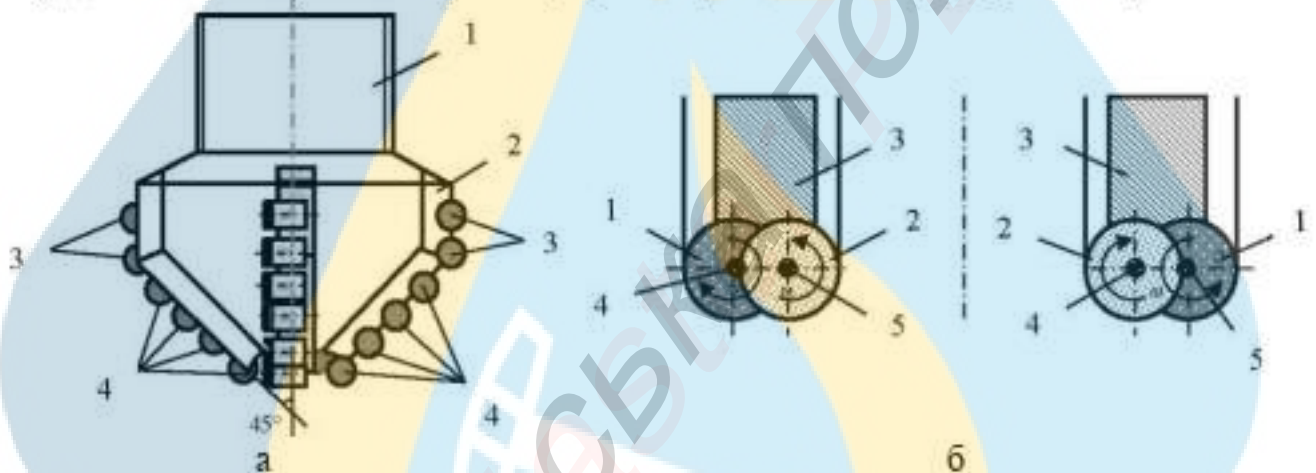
Породоруйнівний інструмент з обертовими при бурінні різцями типу PDC: а) бурове долото: 1 - корпус з різьбленням; 2 - матриця; 3 і 4 - обертові різці; б) бурова коронка: 1 - зовнішній скважинообразуючий різець; 2 - внутрішній кernoобразуючий різець; 3 - матриця коронки; 4 - вісь обертання зовнішніх скважинообразуючих різців; 5 - вісь обертання внутрішніх кernoобразуючих різців; б - елементи каркаса осей обертання різців
